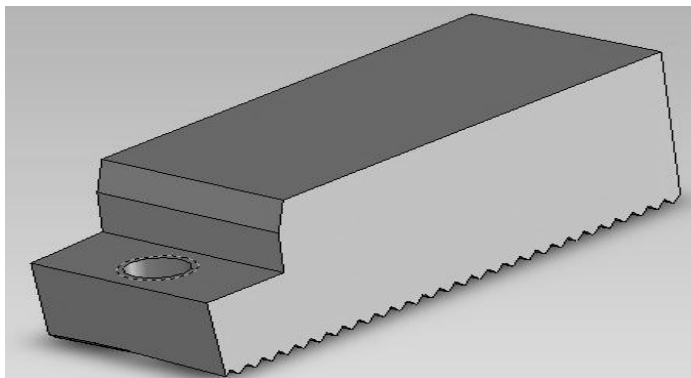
Корпус ножа сборной дисковой фрезы
